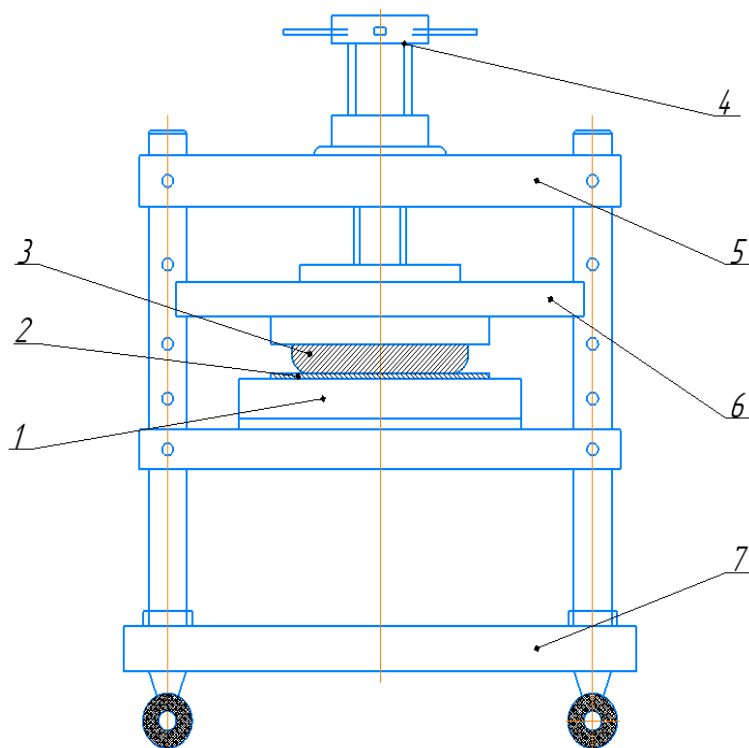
Схема пресса портального типа с механическим приводом:
